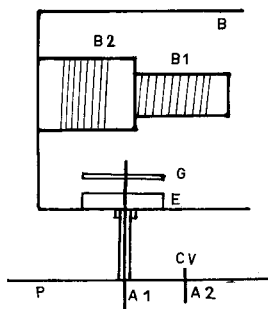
Montage mécanique de l'étage PA (1/4 grandeur, vue dessus)
